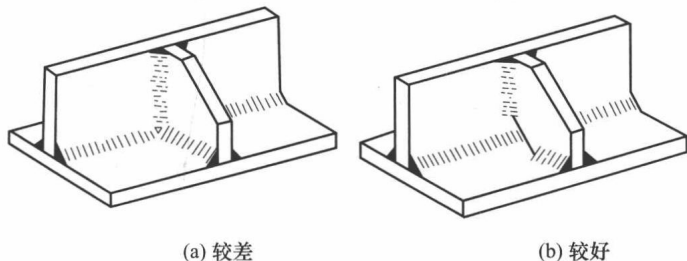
焊缝布置应有利于减少焊缝应力
